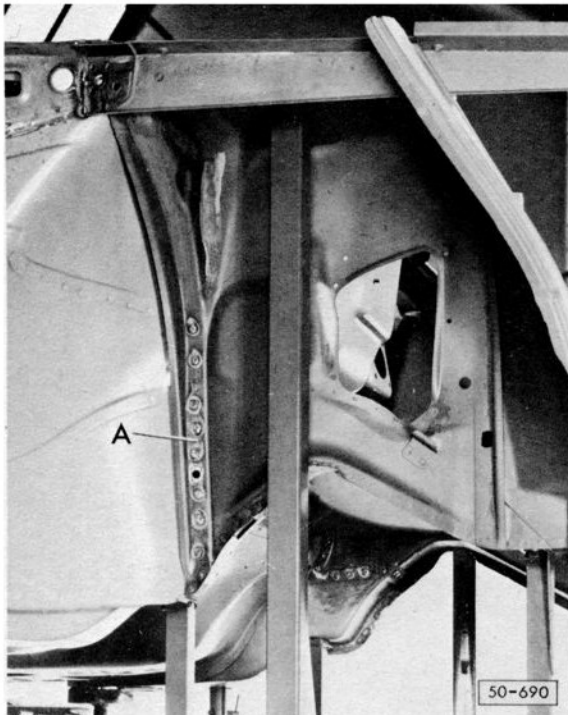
Vorderwagen-Neuteil einschweißen
